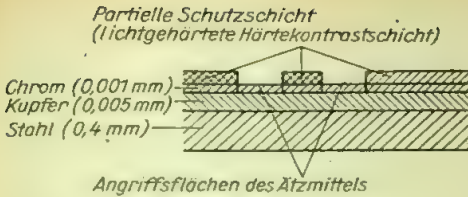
Herstellung einer Flachdruckätzung (Trimetalldruckform)
